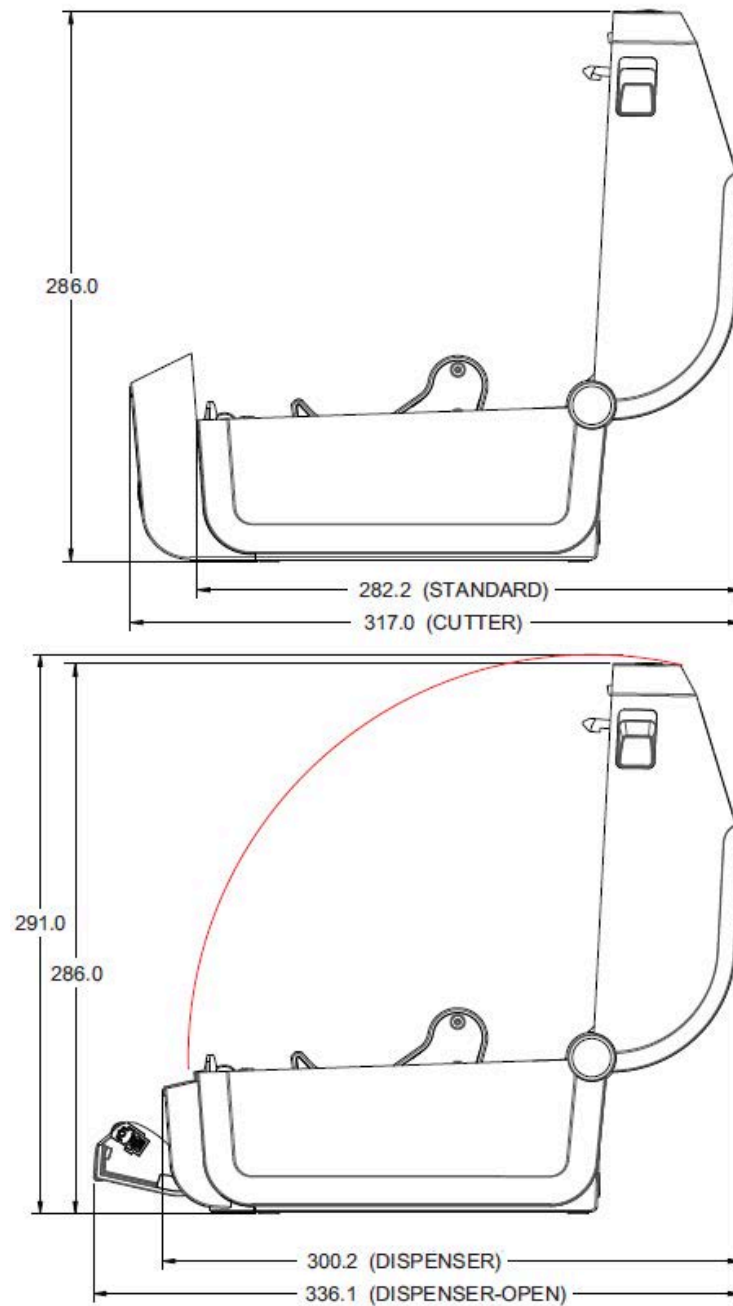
Стандартный принтер для прямой термопечати + дополнительные замок и ключ запирающегося отсека для носителя (1)
